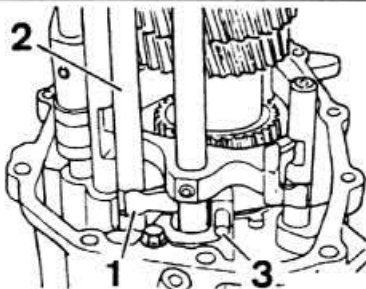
Установка рычага привода промежуточной шестерни заднего хода:
